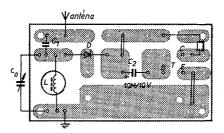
Rozmístění součástek pro zapojení z obr. 4, AR 1/71
